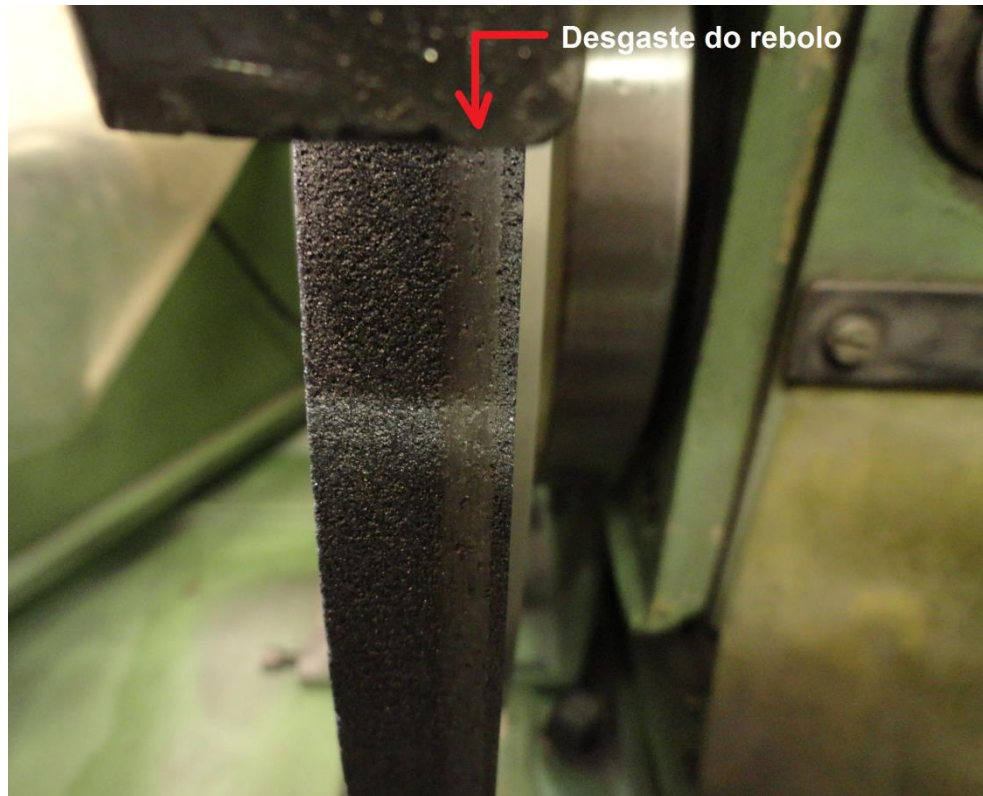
Rebolo de CBN com desgaste após usinagem de um corpo de prova
